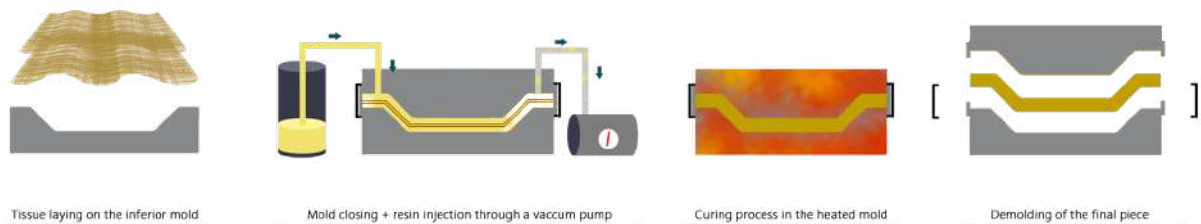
esquema de moldeado térmico, Fuente: composites-ate.com
